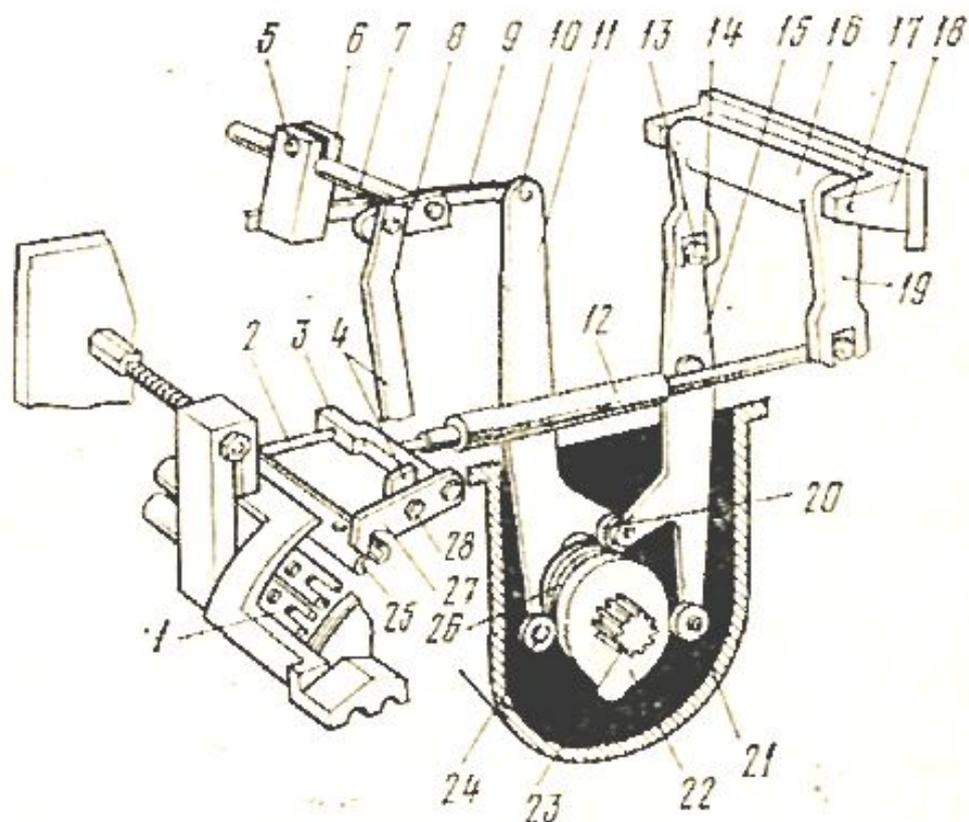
Раскрыватель пружины и выталкиватель прокладчиков утка: 1- прокладчик утка, 2- выталкиватель, 3-штанга, 4-тяги, 5-болт, 6- серьга, 7- валик, 8- плечо валика, 9- тяга, 10-болт, 11- трехплечий рычаг, 12- втулка, 13- сухарик, 14-эксцентрическая ось, 15- трехплечий рычаг, 16- двухплечий рычаг, 17- ось рычага, 18- кронштейн, 19-длинное плечо рычага, 20 и 21 – ролики, 22- спаренный кулачок, 23- кулачковый вал, 24- ролик, 25- пружина прокладчика, 26- спаренные кулачки, 27- раскрыватель пружин, 28-болт.
